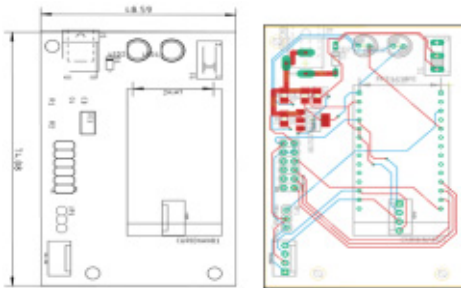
운동 정보 자동 취득 장치 PCB 패턴 결과
